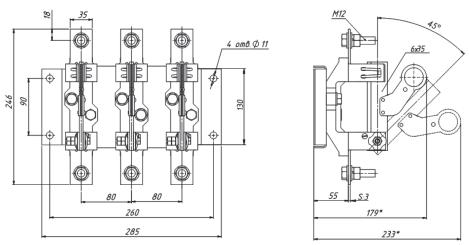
Разъединитель Р43 с пополюсным оперированием штангой ШО-1 на номинальный ток 250 A и 400 A
